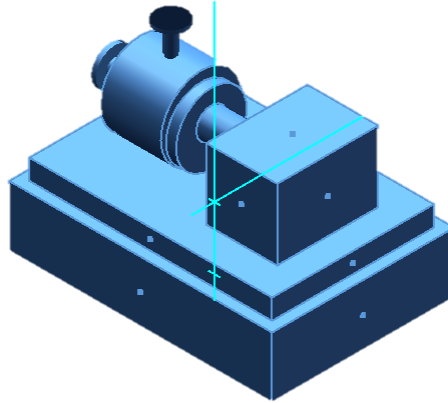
Hasil pemodelan 3D *equipment V-102.
